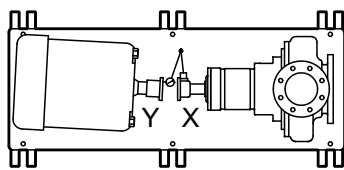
Vue en plan d'un alignement vertical incorrect
